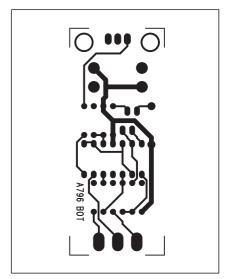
Obrazec desky spojů PWM kontroleru (strana TOP)
